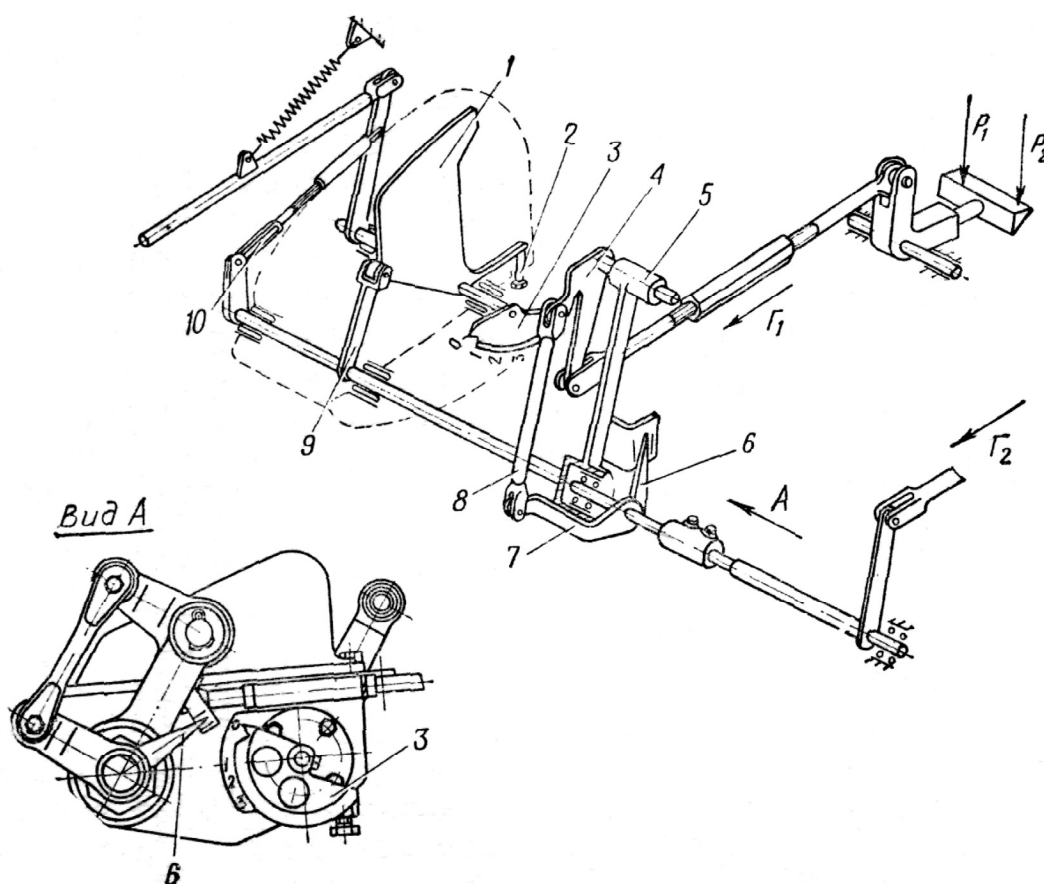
Уравнильное устройство: 1 – кулак; 2 – ограничительный болт исходного положения; 3 – стрелка-указатель; 4 – двуплечий рычаг; 5 – балансир; 6 – стрелка уравнивателя; 7 – рычаг; 8 – тяга; 9 – поводок; 10 – тяга сервомеханизма
